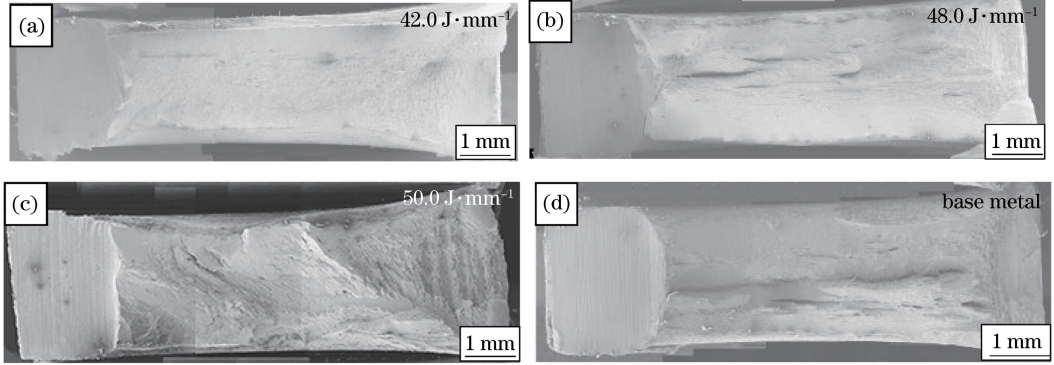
不同热输入下得到的接头焊缝和母材的冲击断口形貌
